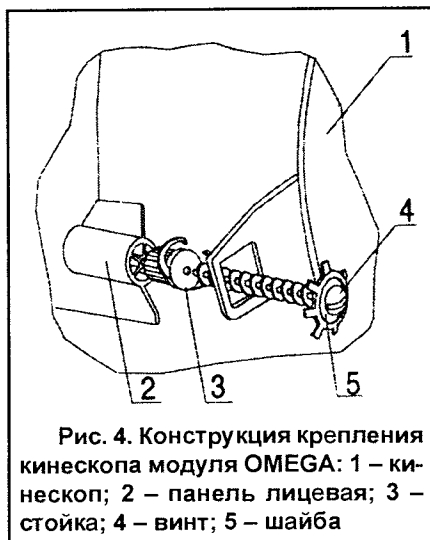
Конструкция крепления кинескопа модуля OMEGA: 1 – кинескоп; 2 – панель лицевая; 3 – стойка; 4 – винт; 5 – шайба
